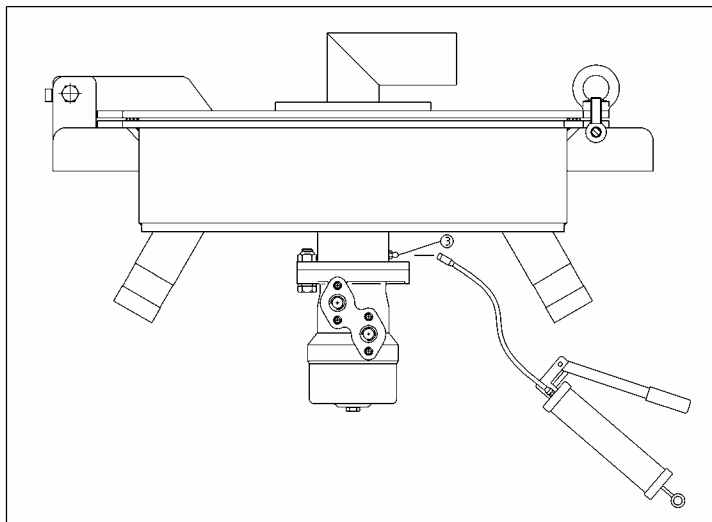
Ölmotoraufnahme / Fig. 5.1 Hydraulic motor holding fixture
